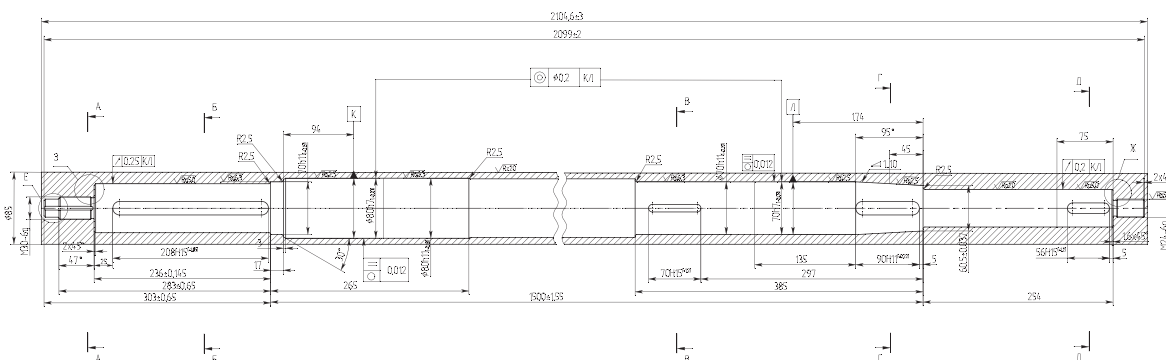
Вал «битера» зерноуборочного комбайна «Вектор».
